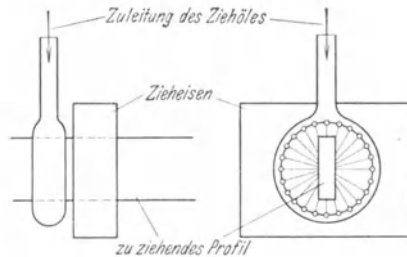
Zuführung des Öls bei schwierigen Profilen.
